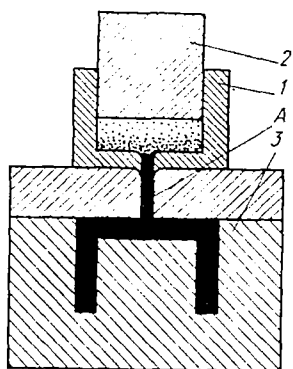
Схема работы пресса для трансферного прессования с передаточной камерой
